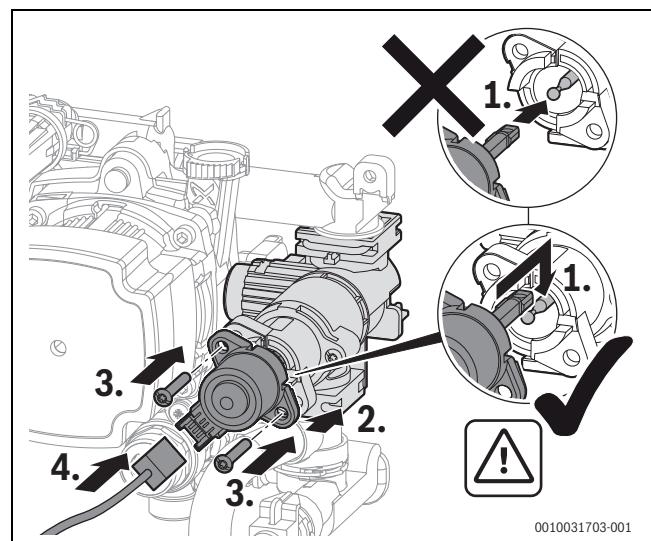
Remonter le moteur au niveau de la vanne sélective (variante avec vis)
